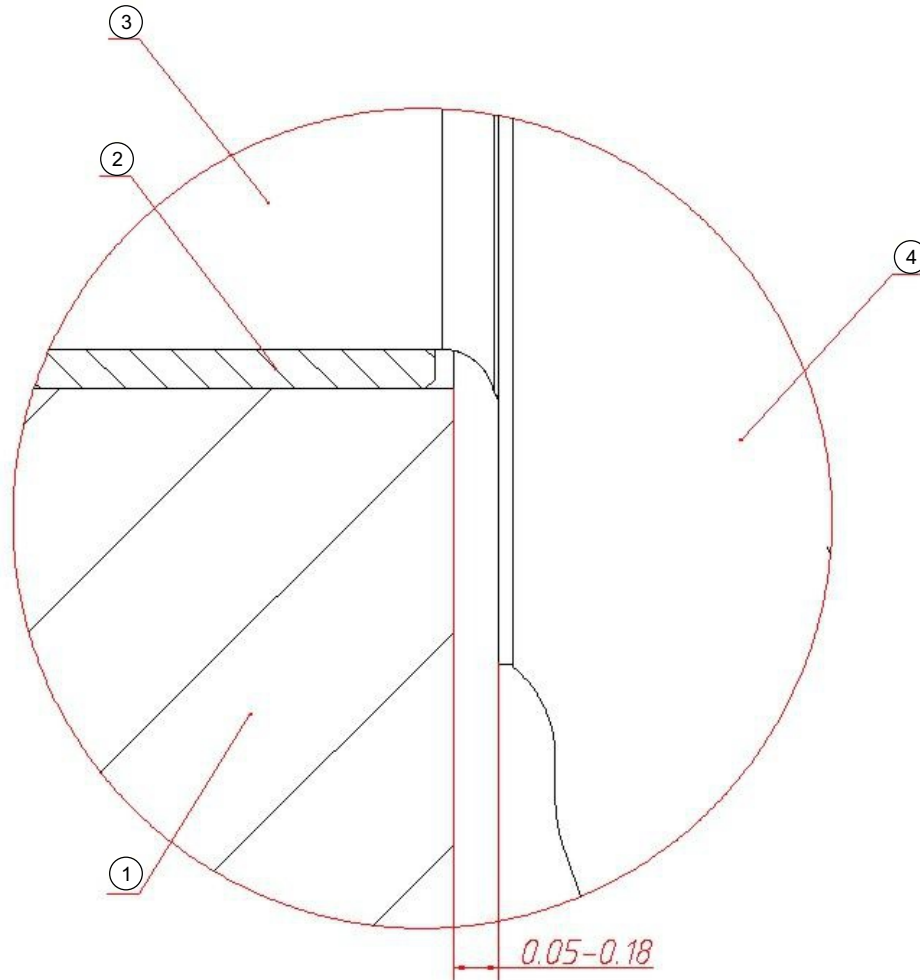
Зазор: торец нижней головки шатуна - торец щеки
